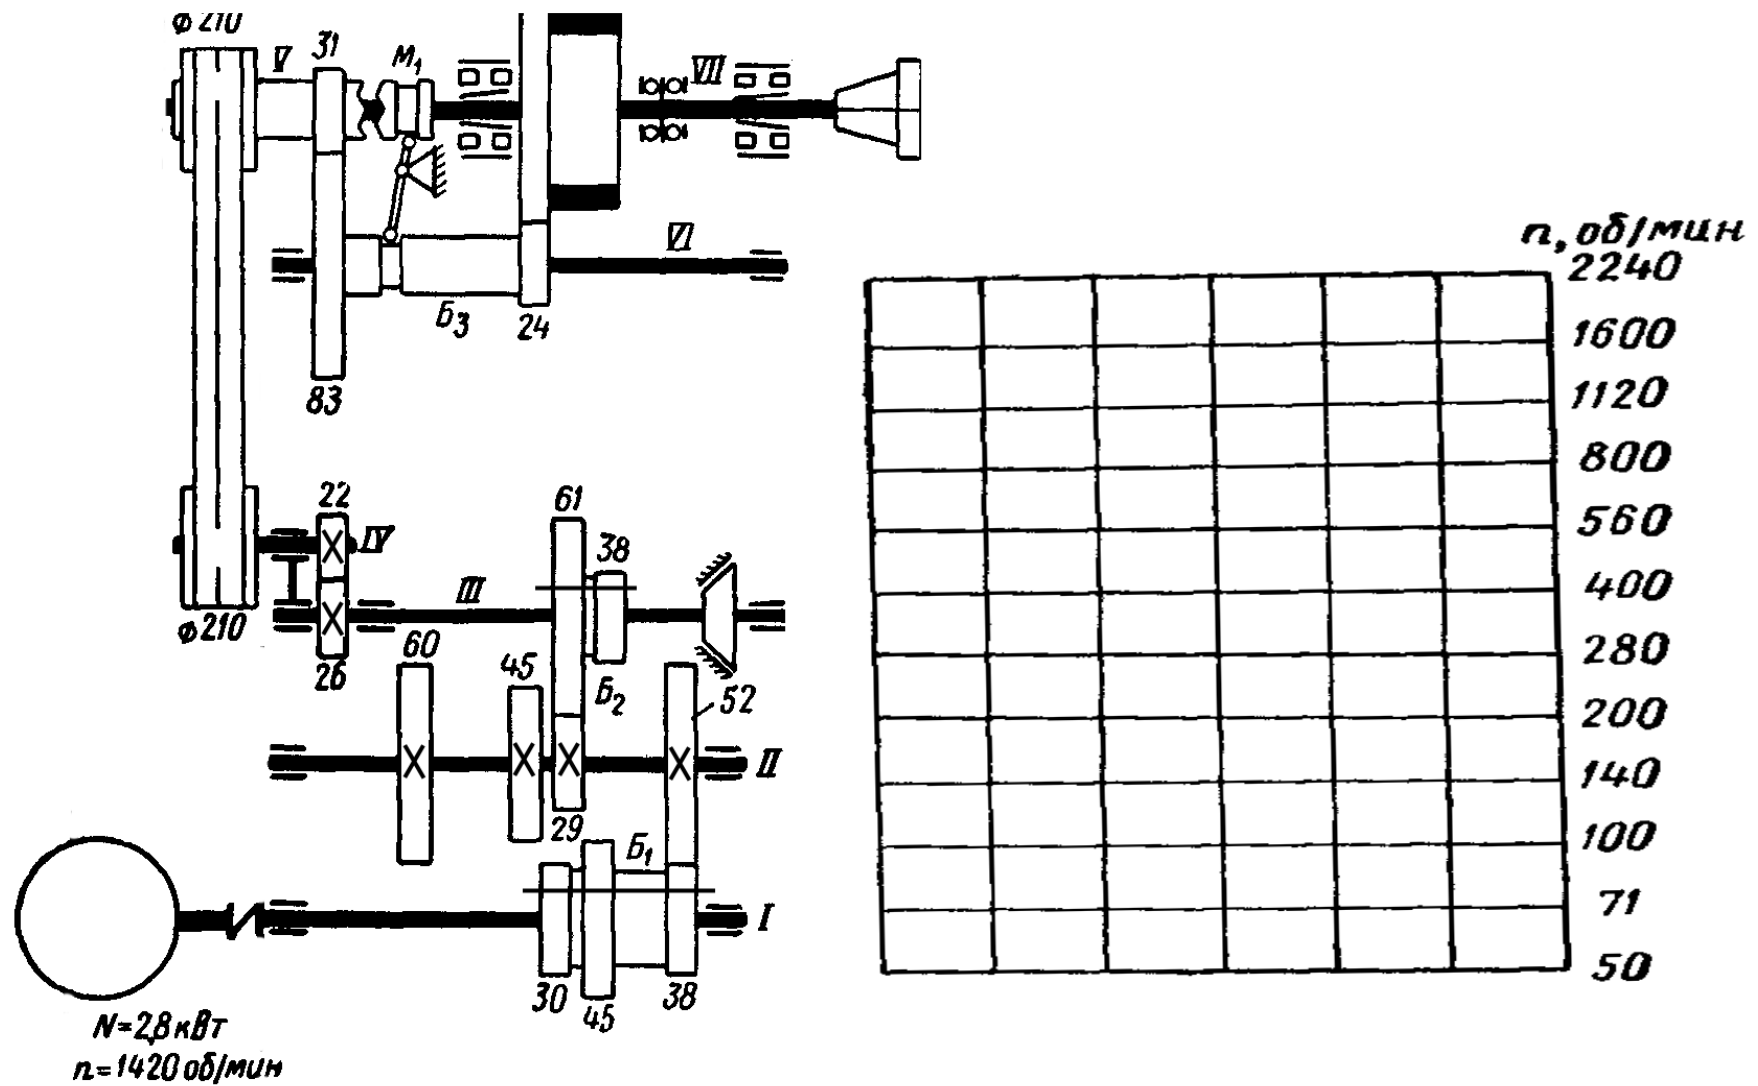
Типова коробка передач фрезерного верстата.
